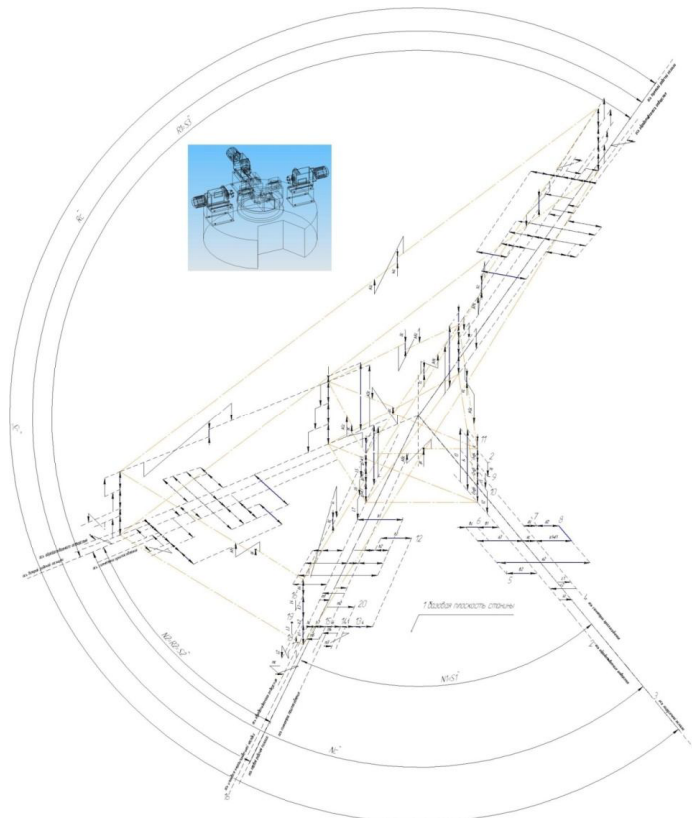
Трехмерная модель многопозиционного агрегатного станка и размерные цепи к ней.
